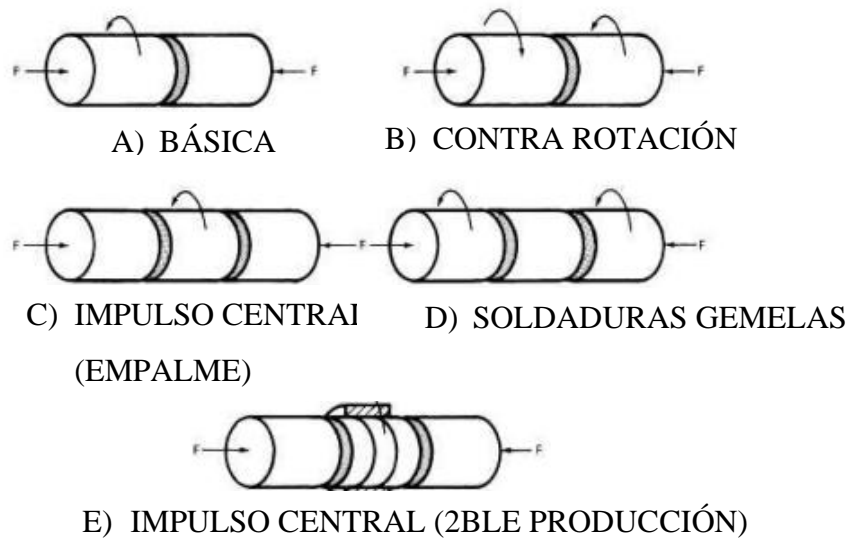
Disposiciones típicas de soldadura mediante fricción [7].
